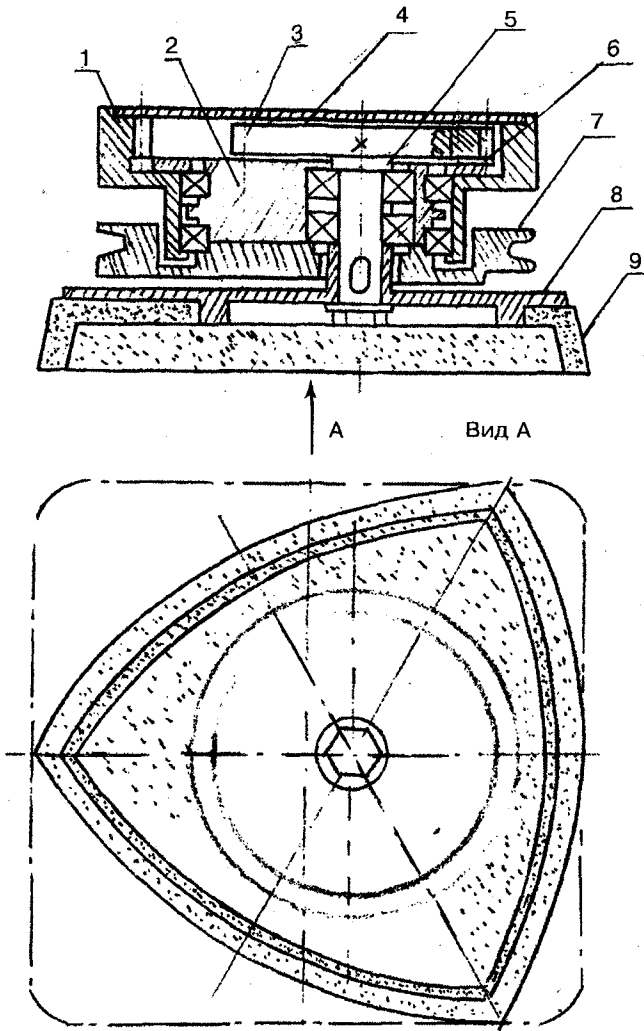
Планетарный механизм: 1 – зубчатое колесо; 2 – водило; 3 – шестерня; 4 и 6 – подшипники; 5 – вал; 7 – ведомый шкив; 8 – планшайба; 9 – рабочий инструмент
